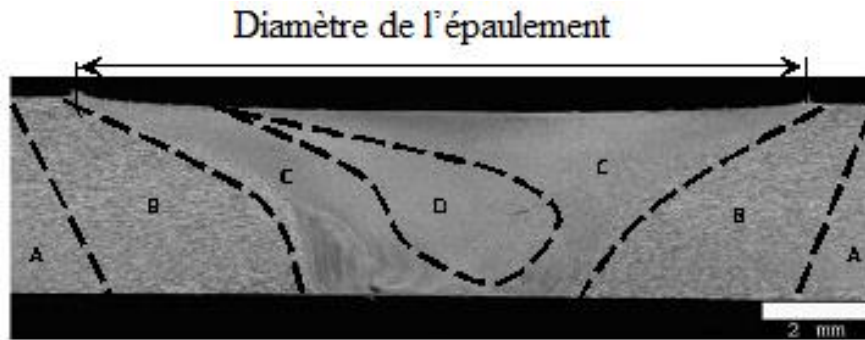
Coupe d'une soudure sur un alliage d'aluminium 6061-T6 [62], [63] et [64].
